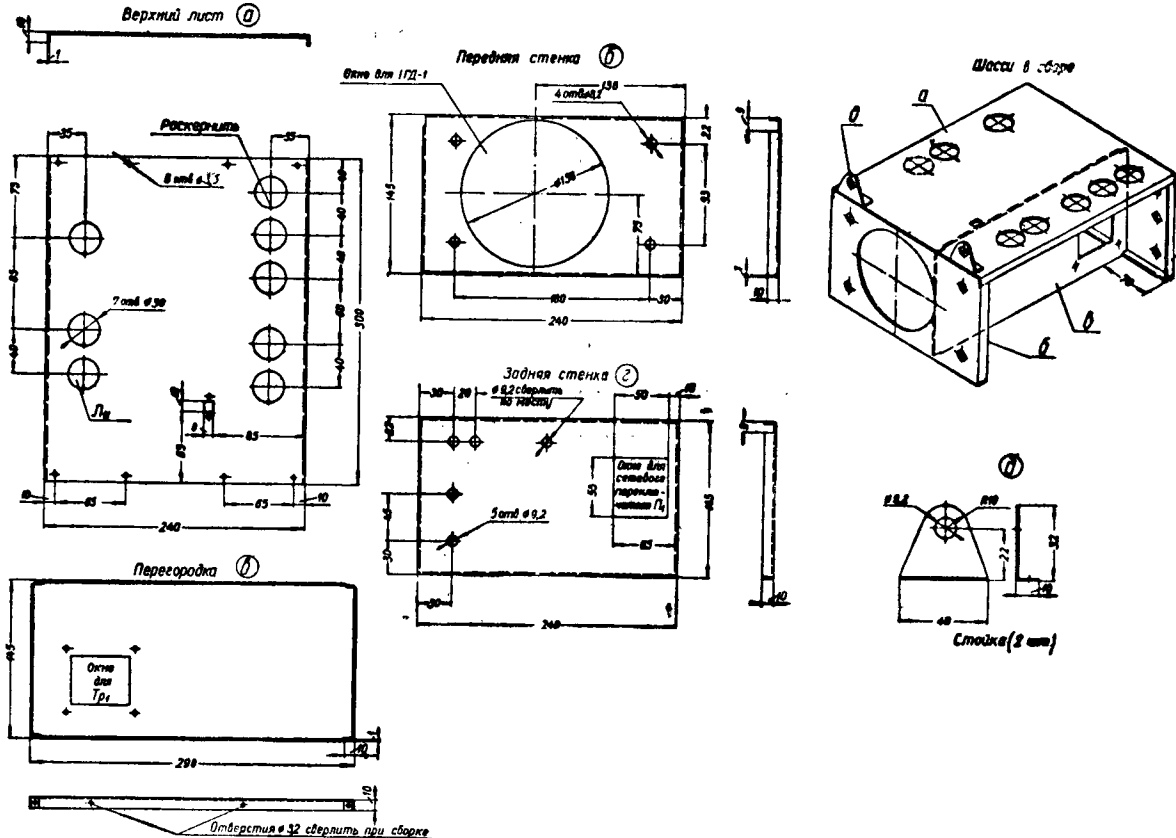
Детали и общий вид шасси: а — верхний лист; б — передняя стенка; в — перегородка; г — задняя стенка; д — стойка для крепления сопротивлений
